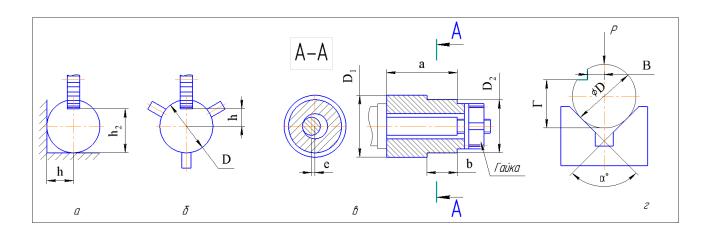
Способы установки вала в приспособлении: a – вал прилегает к двум плоскостям; б – вал закреплен в 3-х кулачковом патроне; b – вал установлен в жесткую оправку; r – вал установлен в призму
